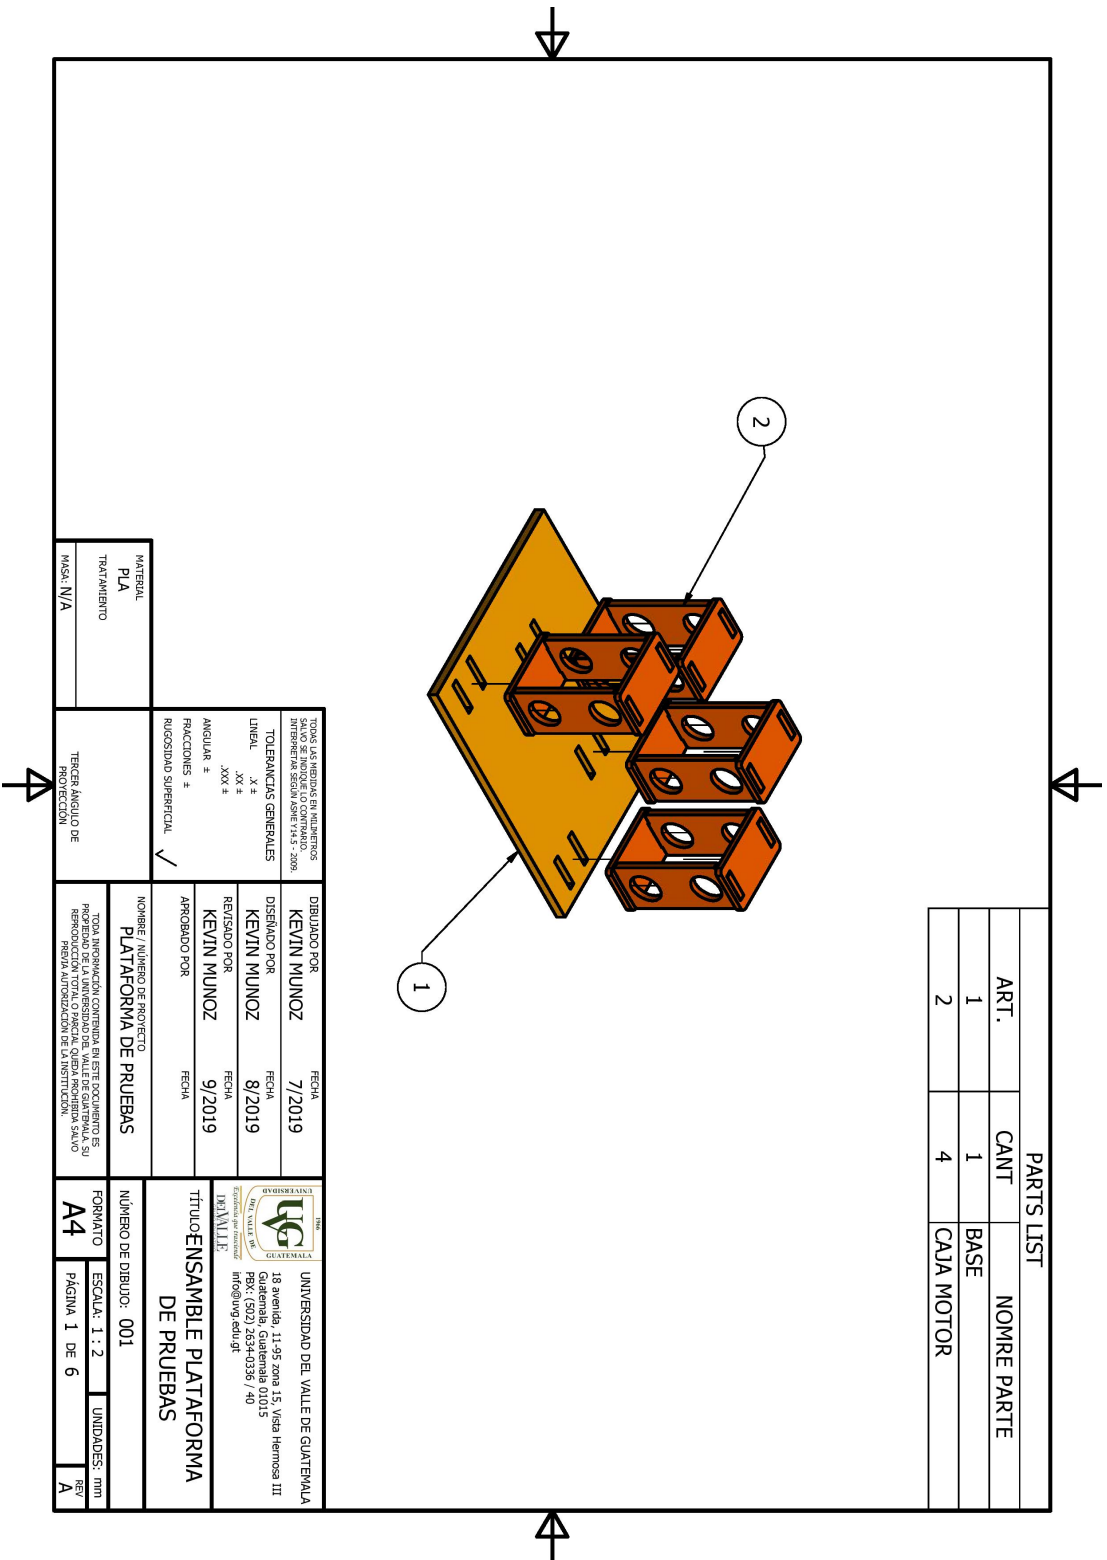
Plano de explosión de ensamble de plataforma de montaje
